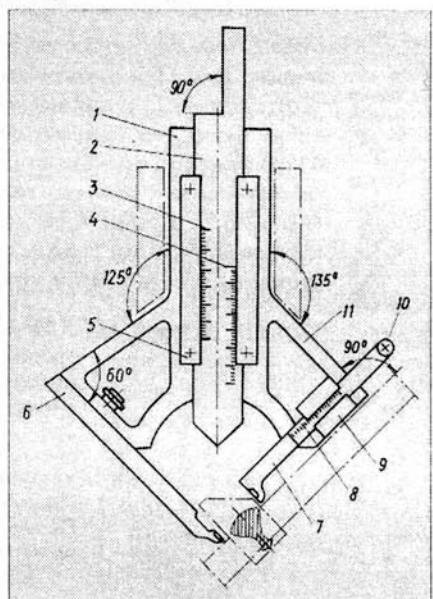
Приспособление для замера конструктивных элементов сварных соединений на базе шаблона Ушерова-Маршака:
